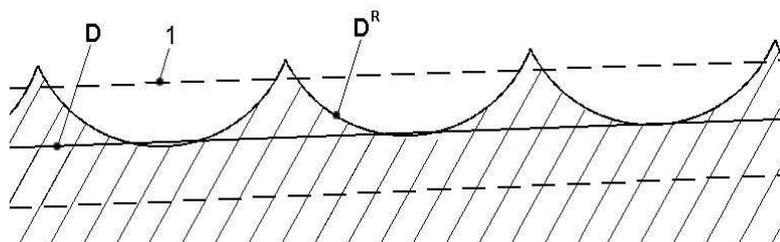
Формирование детали следовыми поверхностями инструмента: D – поверхность аналитического эталона детали; D^R – следовые поверхности фрезы; 1 – верхнее значение допустимого отклонения детали
